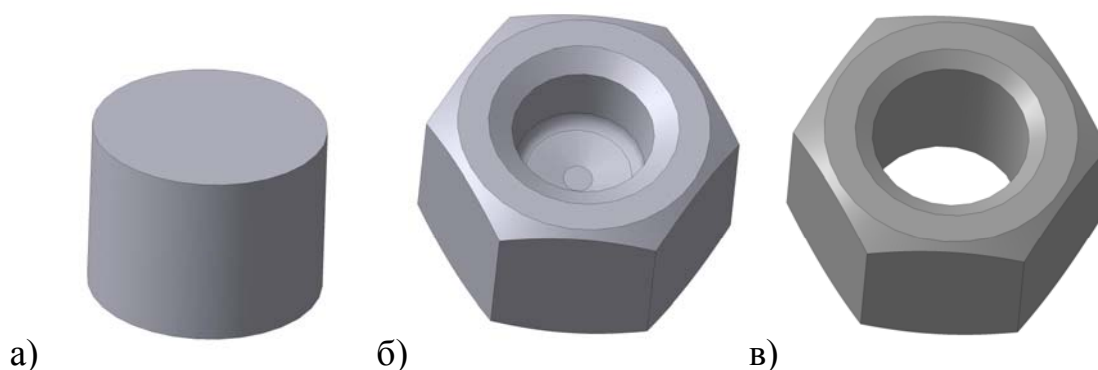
3D модели: а) заготовка; б) поковка гайки; в) гайка
